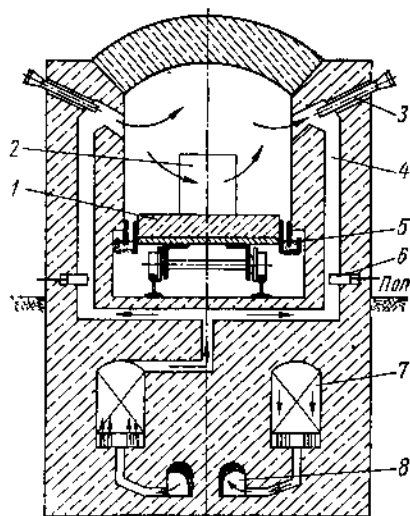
Схема поперечного разреза печи с выдвижным подом (совмещенный разрез)
